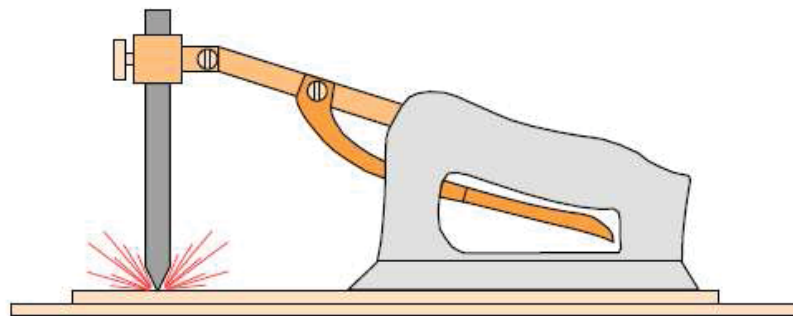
Sistema para soldagem a arco com eletrodo de carvão de acordo com a patente de Bernados
